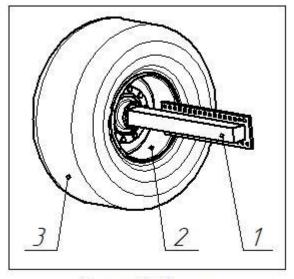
Каретка 1 – Полиось; 2 – Диск; 3 – Шина
